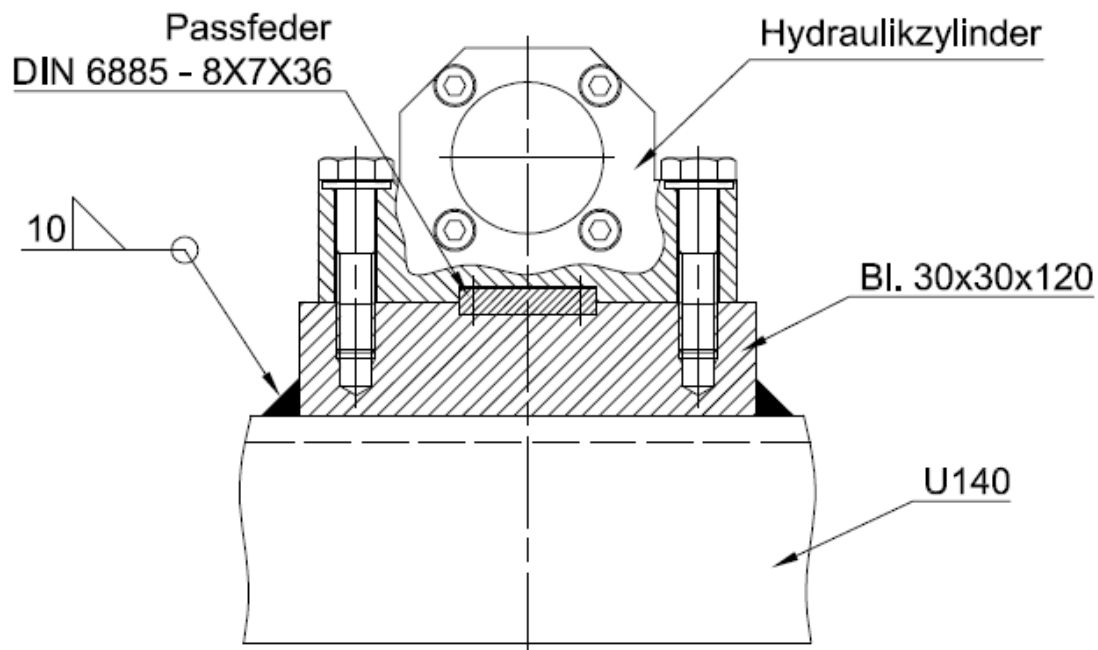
BG11; Detail Montage des Hydraulikzylinders
